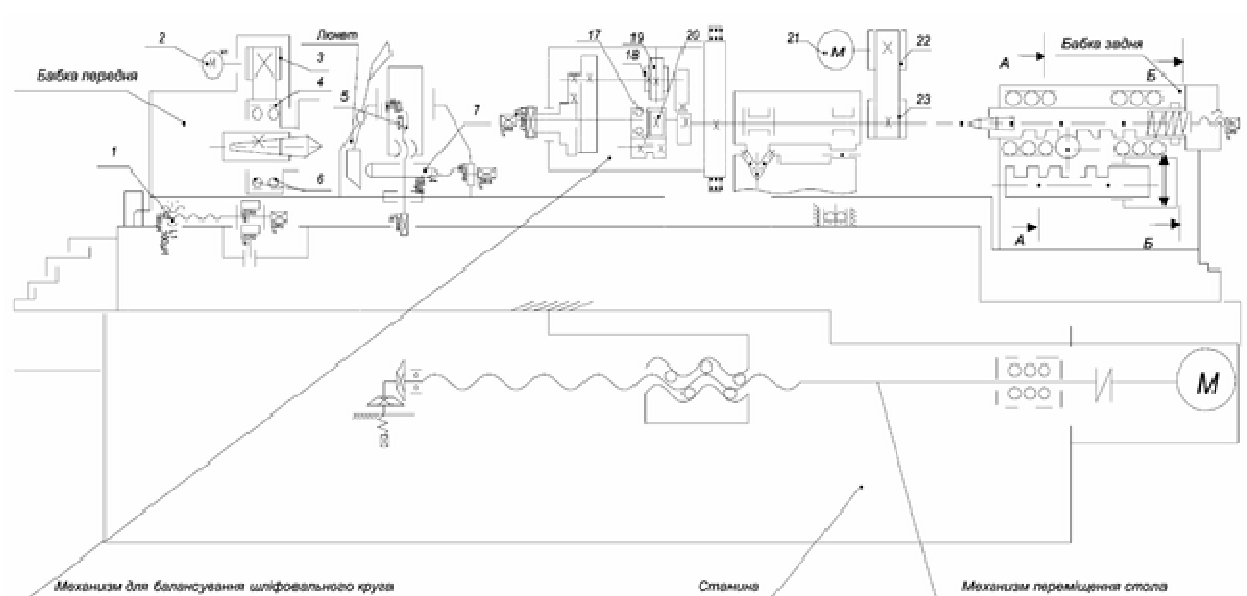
Загальна кінематична схема заточного верстата
